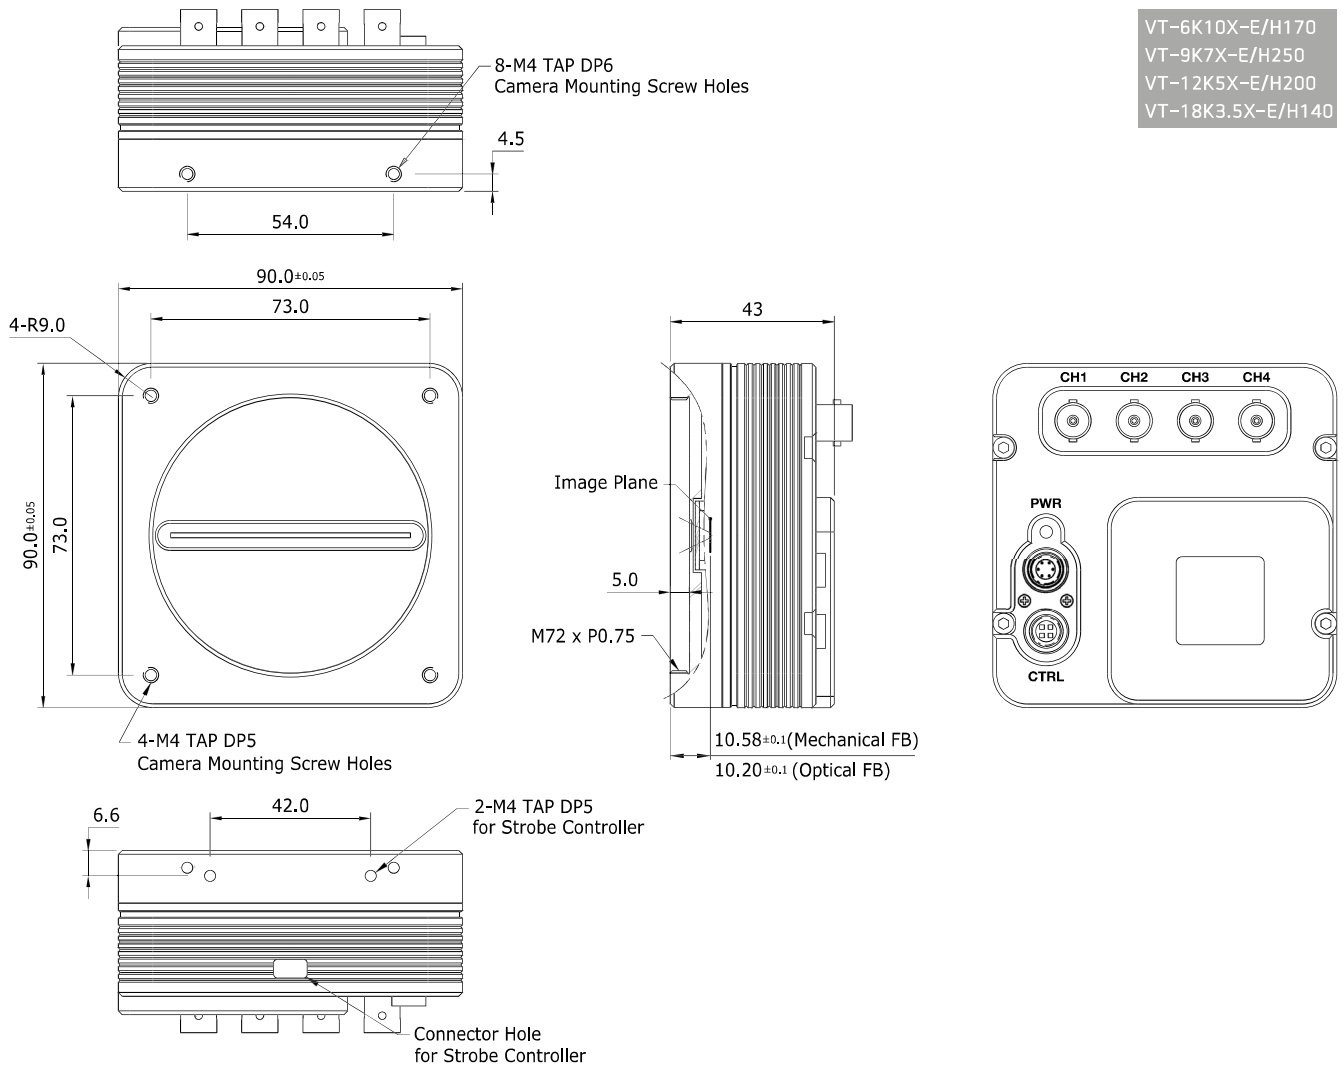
M72 mount 지원 VT CXP Series Mechanical Dimension
